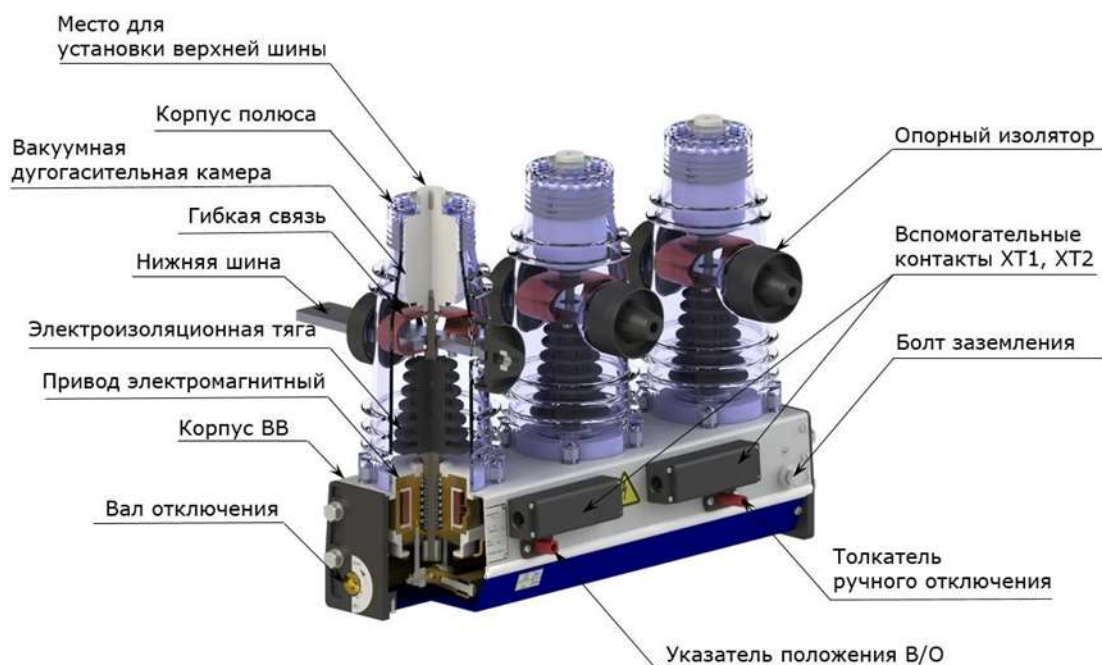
Внешний вид выключателя ВВ/TEL–6
